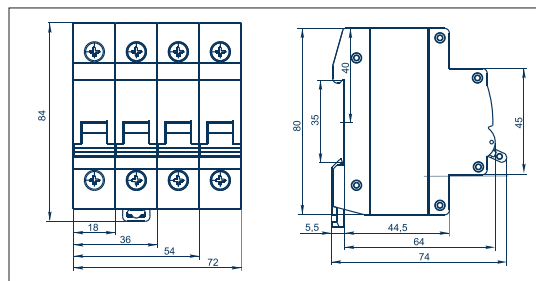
Габаритные и установочные размеры ВН 32-100
